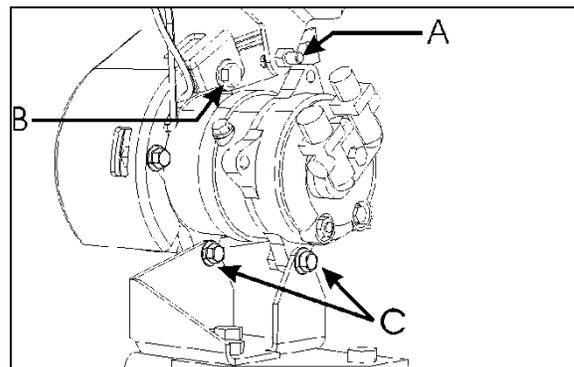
MONTAJE DEL COMPRESOR SERIE H
